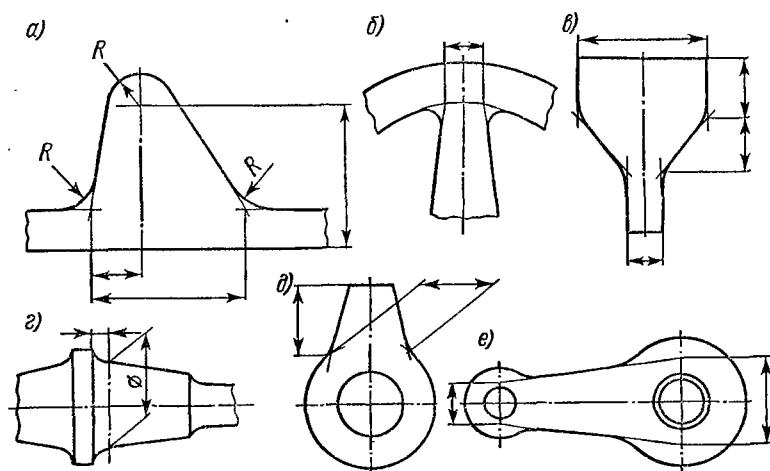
Примеры нанесения размеров деталей с плавными переходами поверхностей
